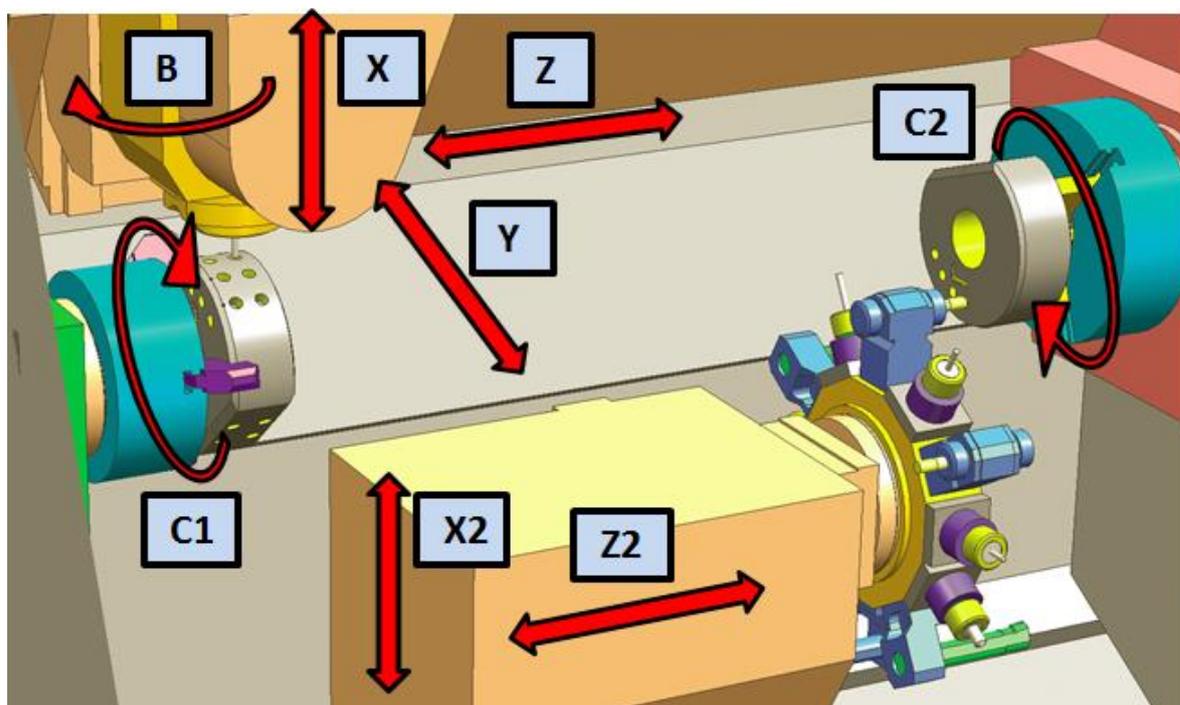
Кинематическая схема токарно-фрезерного ОЦ
